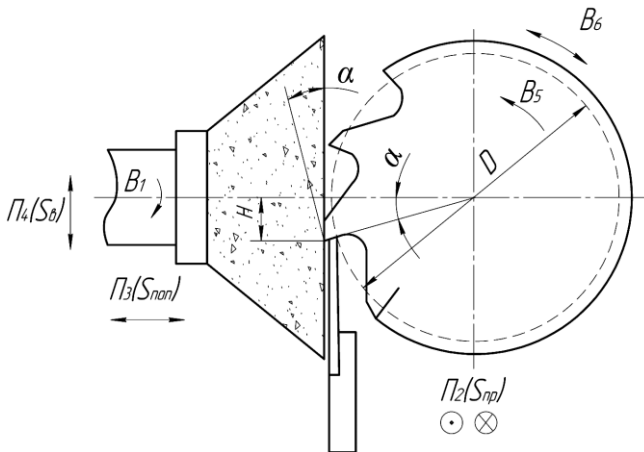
Технологическая схема заточки цилиндрической фрезы по задней поверхности на универсально-заточном станке
